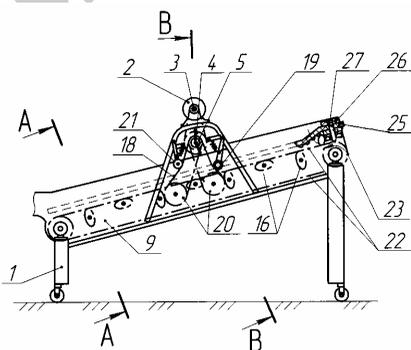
Общий вид машины для сухой очистки картофеля (вид сбоку)
